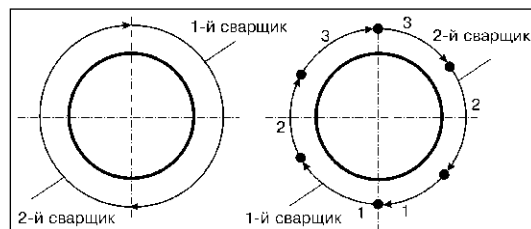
Порядок наложения слоя шва горизонтального стыка при сварке двумя сварщиками
